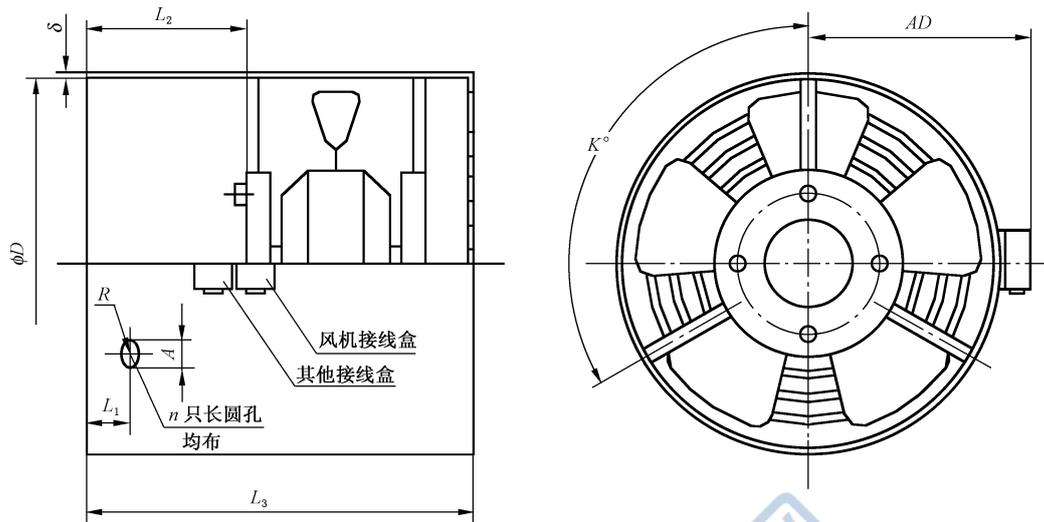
双支撑安装结构的风机安装尺寸和外形尺寸
